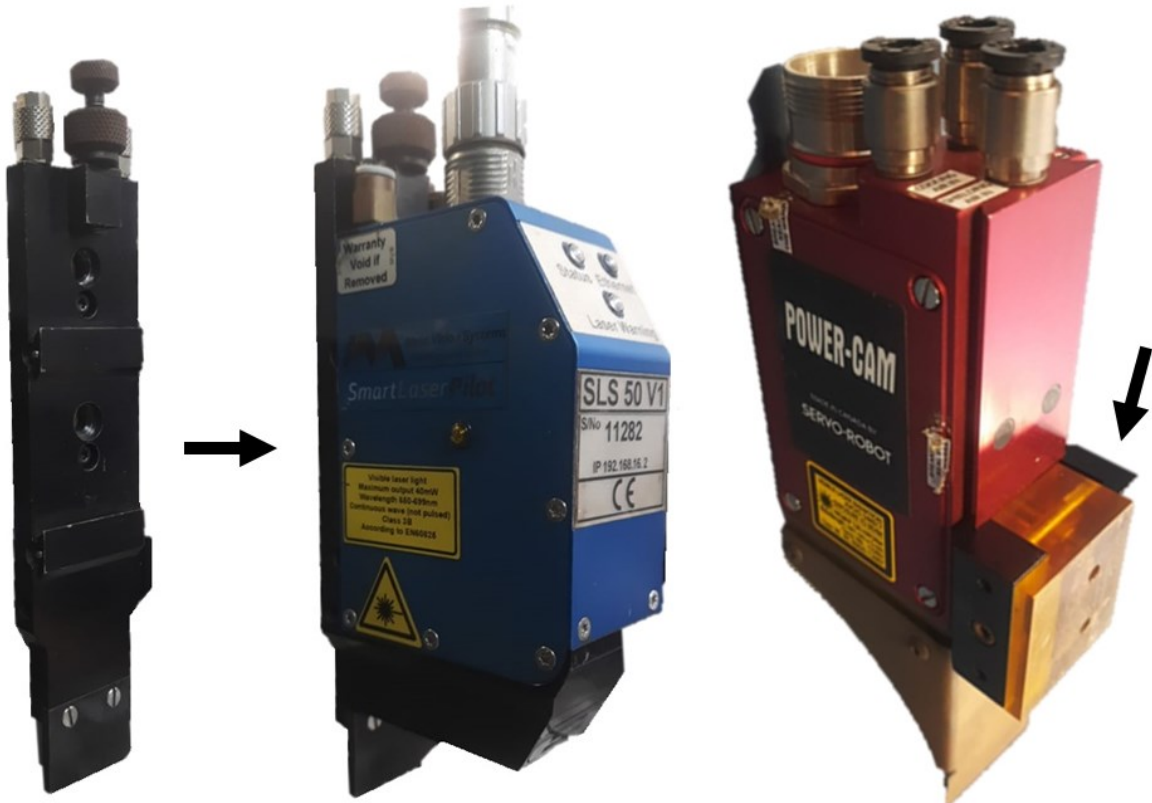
CSI: robô de soldagem interna adaptativa e inspeção, com destaque do STL.
